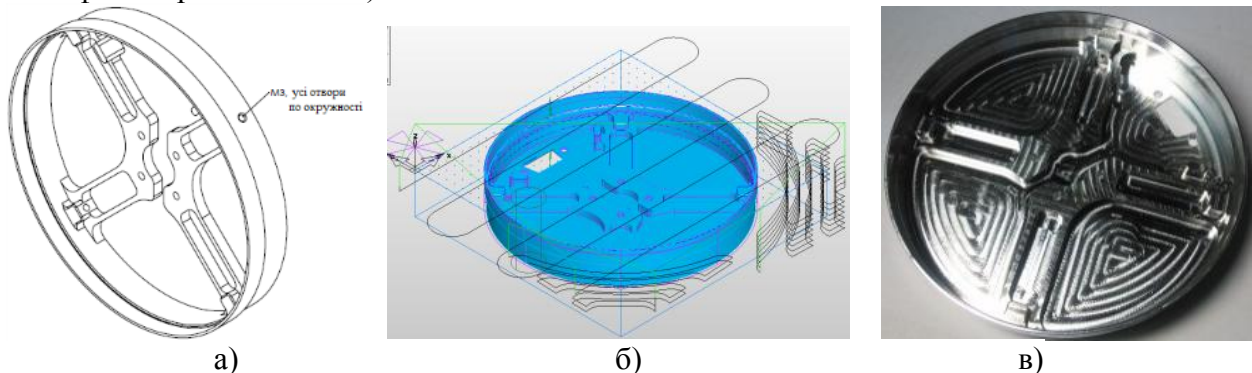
Ескіз а), генерація траєкторій переміщення інструменту при виготовленні деталі б) та готова деталь типу «Корпус» в)
